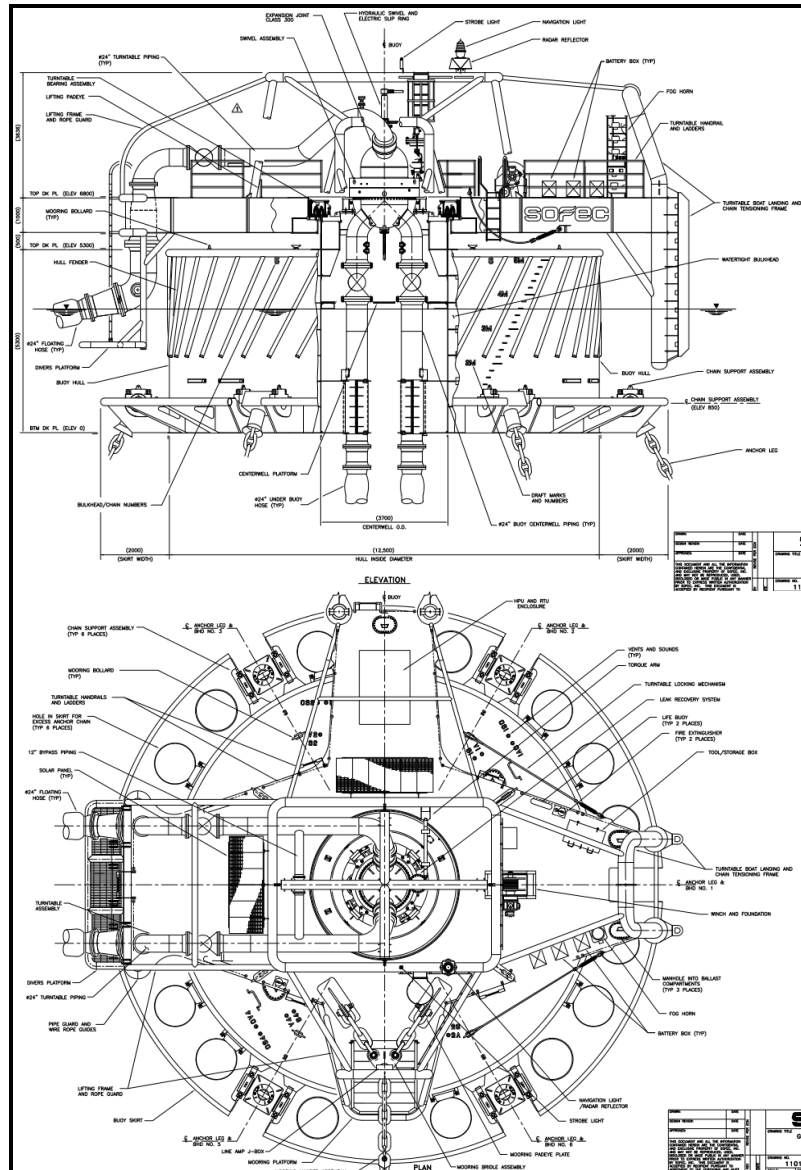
Detalle de la Monoboya propuesta para el Proyecto.
